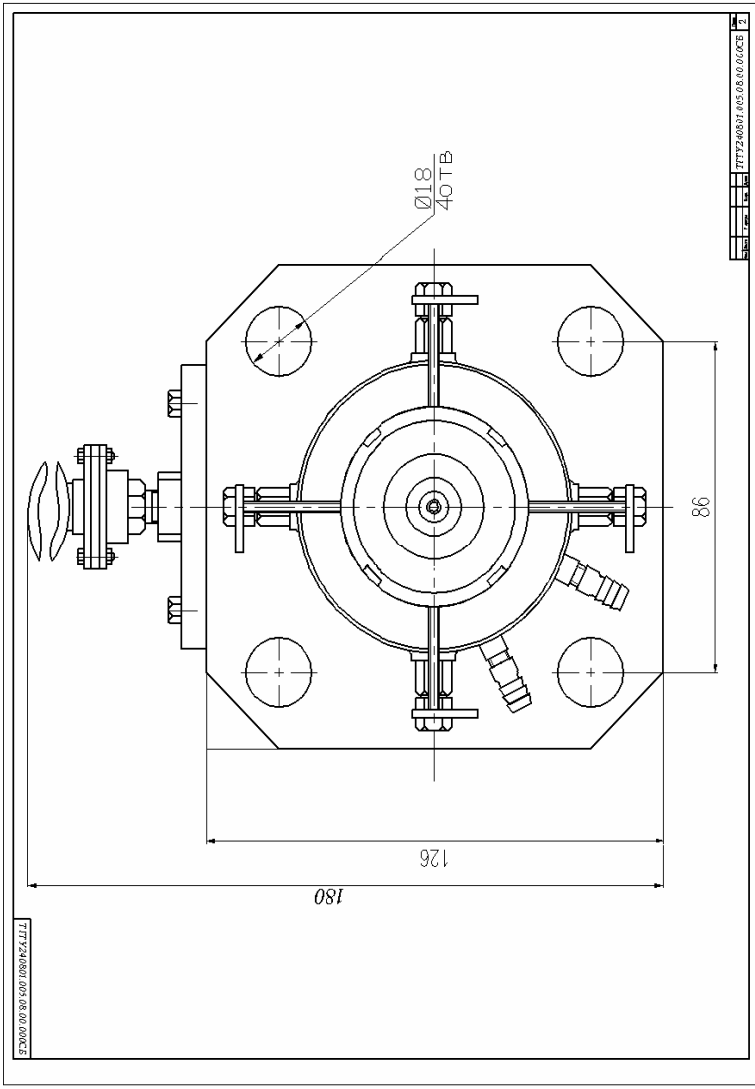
Сборочный чертёж головки прямооточной (лист 2)
